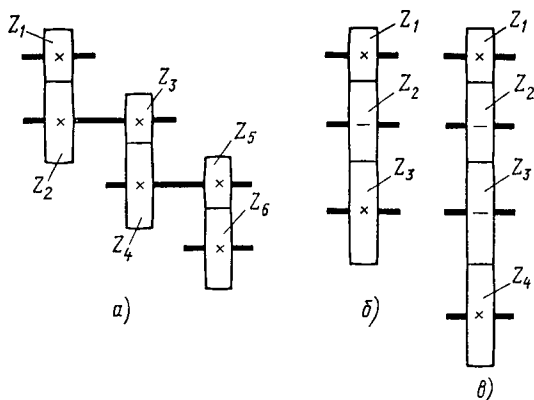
Схемы трехступенчатой (а), с одним паразитным колесом (б) и с двумя паразитными колесами (в) зубчатых передач
